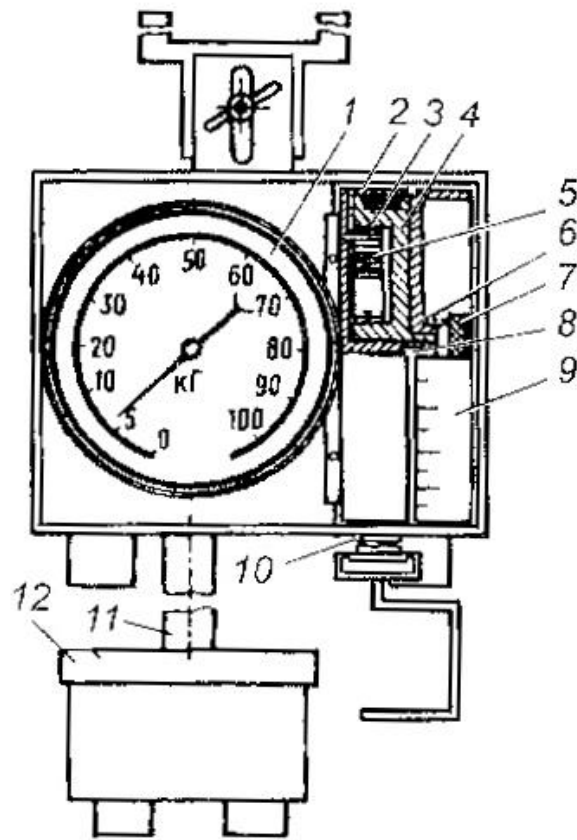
Пристрій для перевірки зчеплення трактора: 1 - манометр; 2 - корпус; 3 – палець; 4 - барабан; 5 - спіральна пружина; 6 - пружина; 7 - гвинт; 8 - шкала; 9 - барабан зі шкалою; 10 - металева стрічка; 11 - шланг; 12 - датчик.
